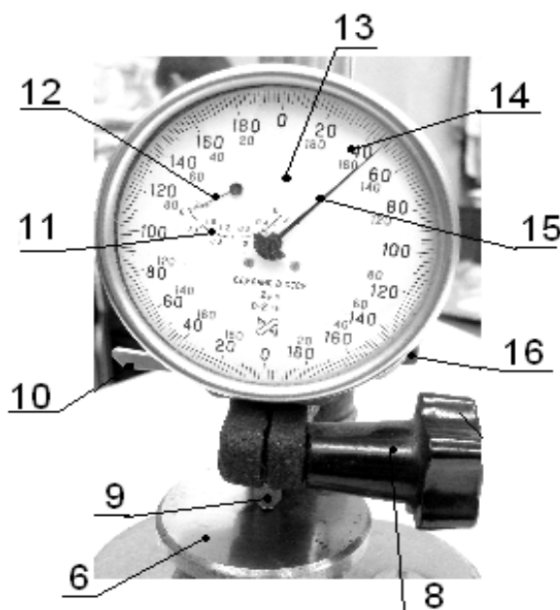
Внешний вид многооборотного индикатора типа 2-МИГ:
